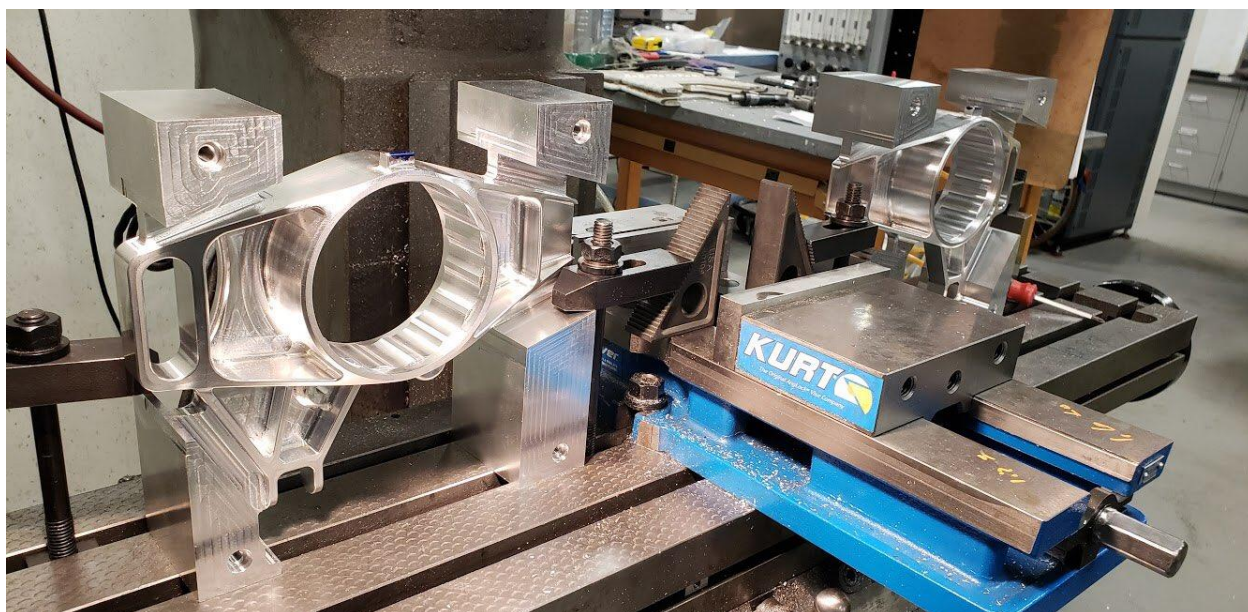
Цельноалюминиевые фрезерованные кулаки
